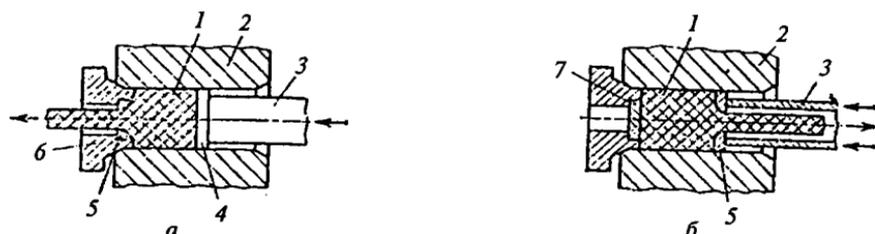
Схема прессования: а — прямое; б — обратное: 1 — заготовка; 2 — контейнер; 3 — пуансон; 4 — пресс-шайба; 5 — матрица; 6 — матрица-держатель; 7 — шайба
